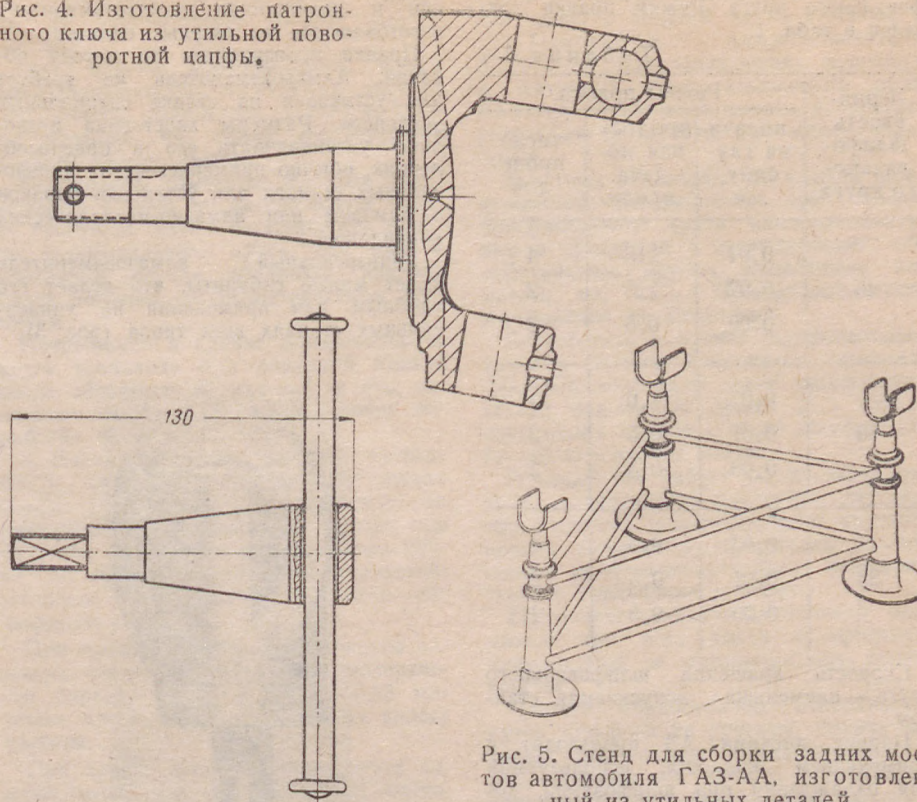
Стенд для сборки задних мостов автомобиля ГАЗ-АА, изготовленный из утильных деталей.
